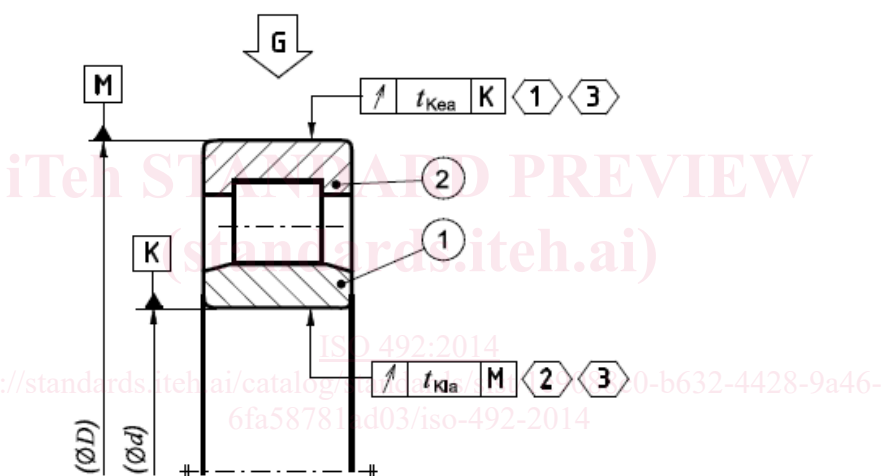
Геометрические допуски отдельных деталей подшипника с цилиндрическим отверстием
